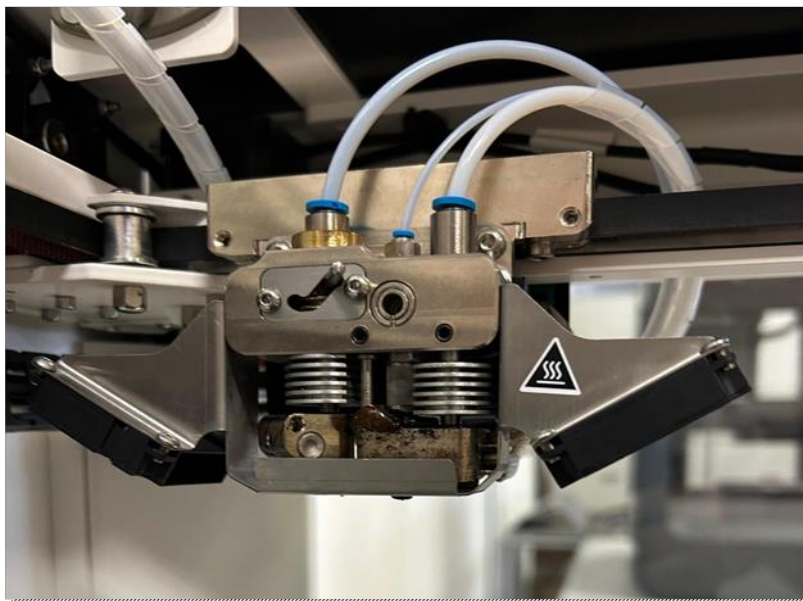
Sistema di estrusione dell'Anisoprint Composer A3
